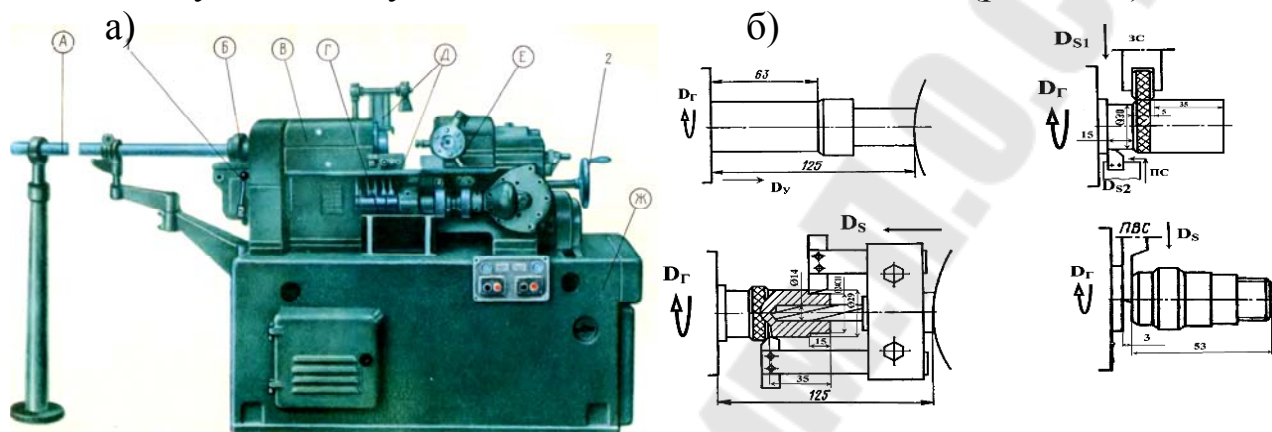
Общий вид токарно-револьверного автомата с горизонтальной осью вращения револьверной головки (а) и схема обработки (б)
